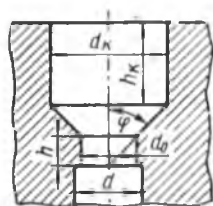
Основные размеры граюры матрицы для горячего прессования
